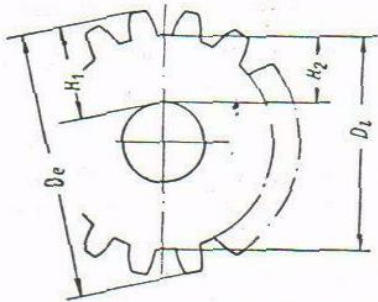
Схема вимірювання висоти зуба штангенциркулем
